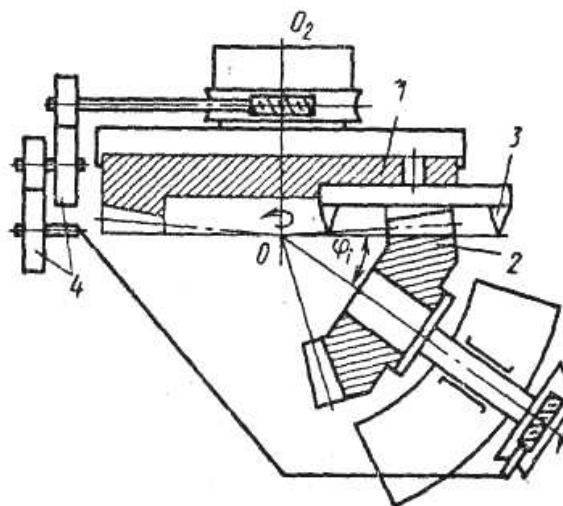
Схема установки заготовки при нарезании круговых зубьев
